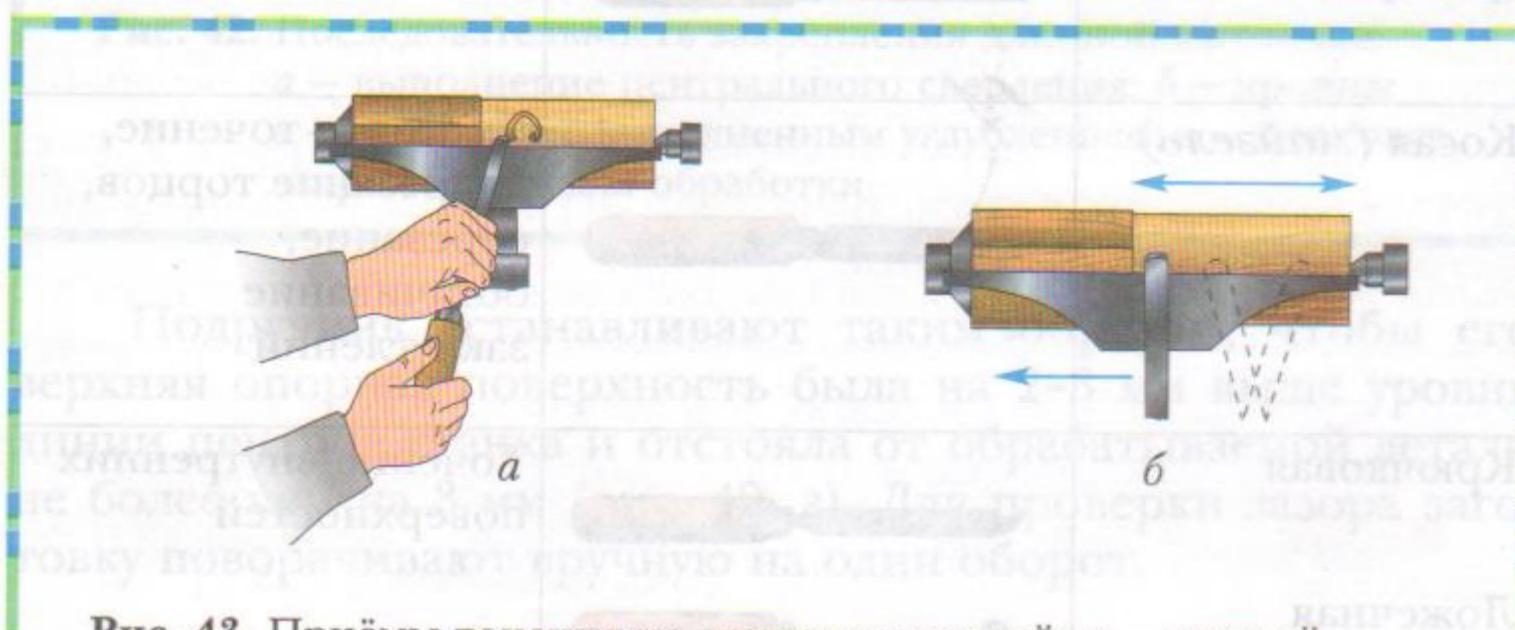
Приёмы точения на станке стамеской: а — первый проход; б — обтачивание разными частями лезвия
